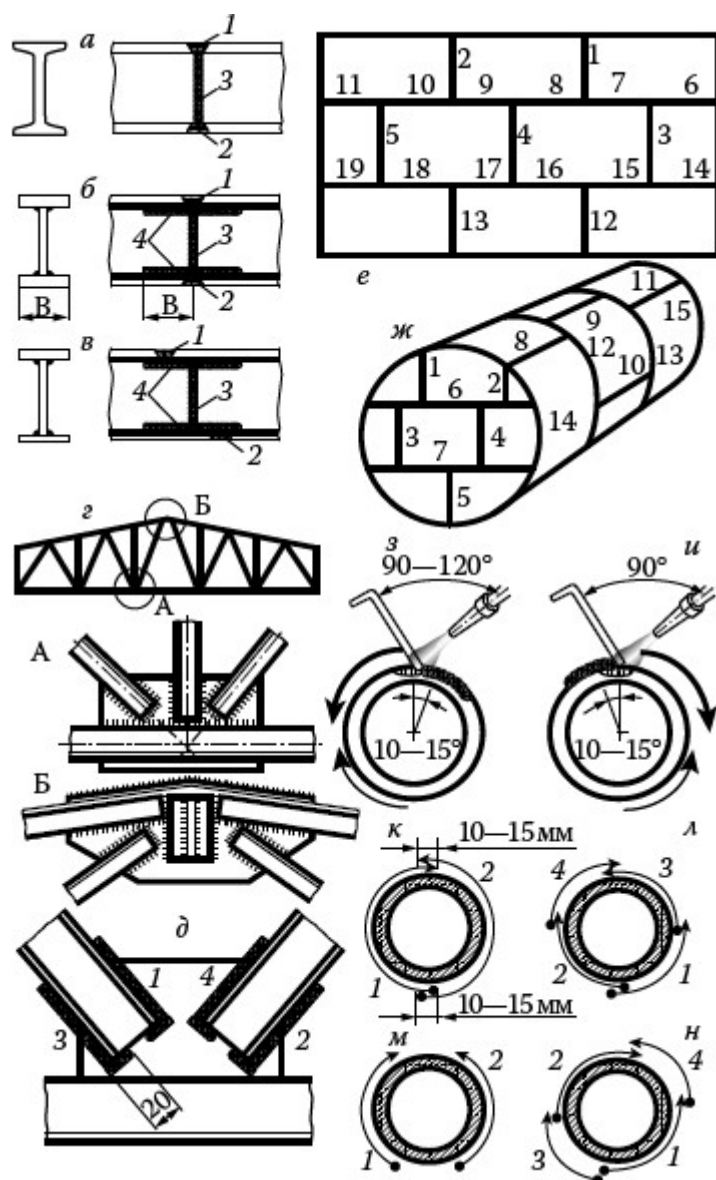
Методы сварки металлоконструкций (цифры обозначают последовательность выполнения швов):
